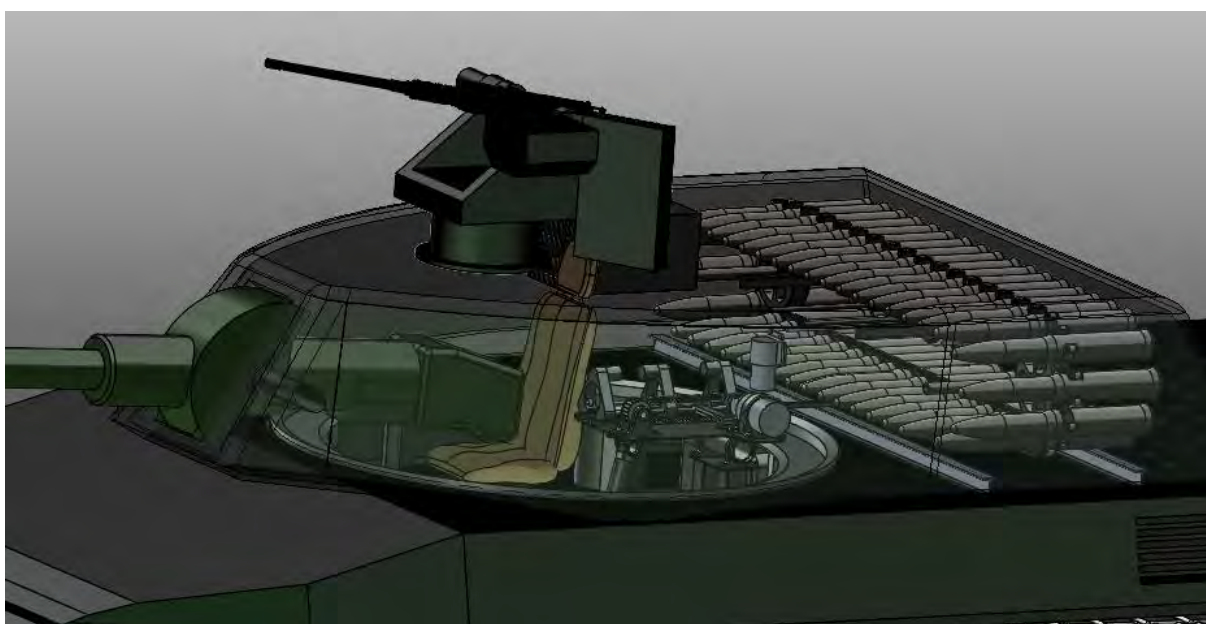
Modelagem CAD 3D do sistema de armamento principal empregado
